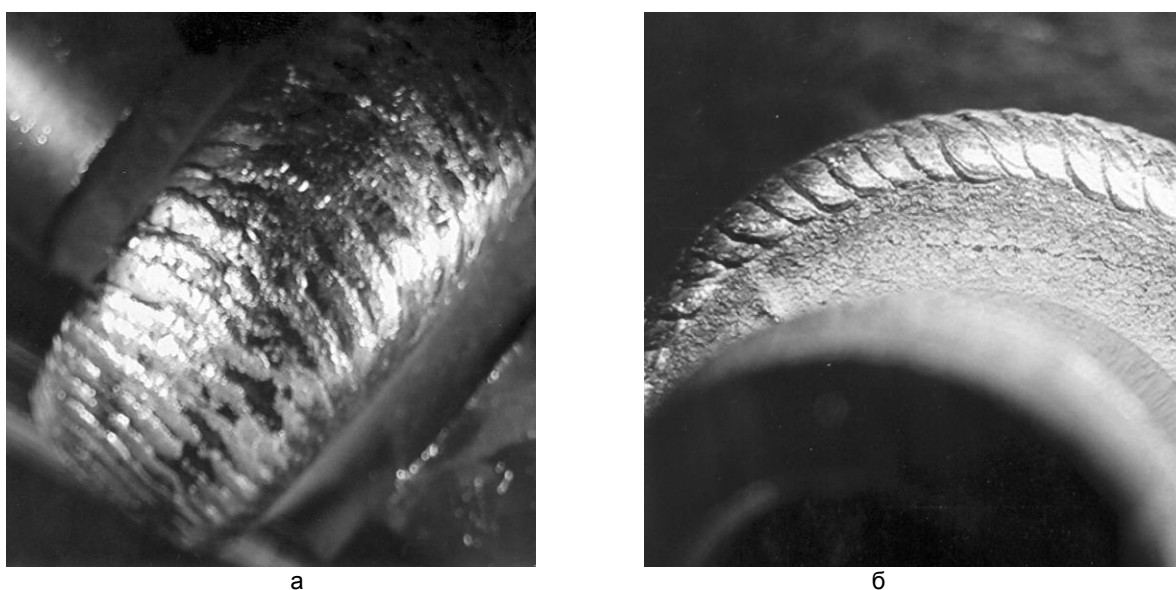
Поверхность шейки распределительного вала двигателя ВАЗ с металлопокрытием, нанесенным широкослойной наплавкой колеблющимся электродом: фронтальный (а) и боковой (б) виды
